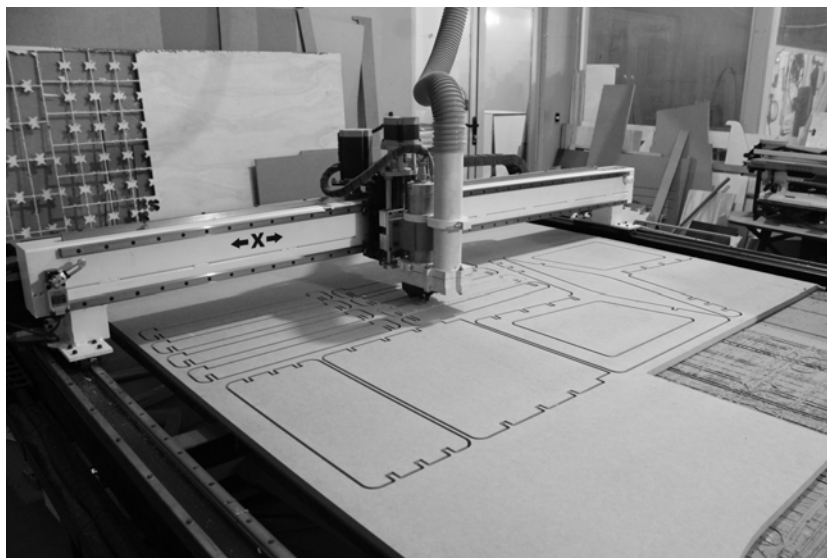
Máquina CNC cortando primeiro protótipo em escala real
